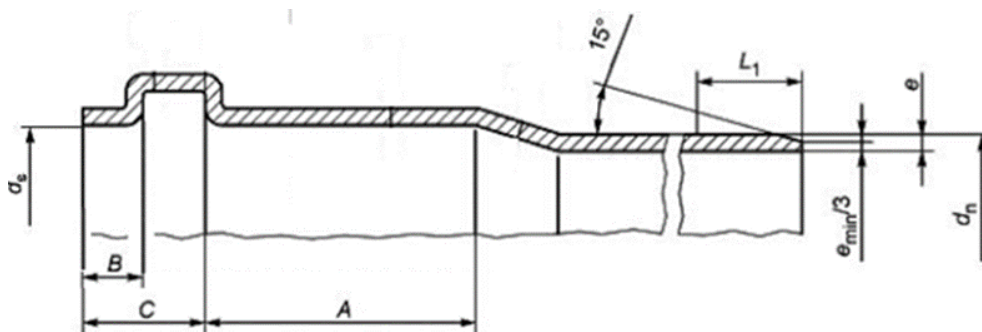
Основные размеры раструба и трубного конца под уплотнительное кольцо.
